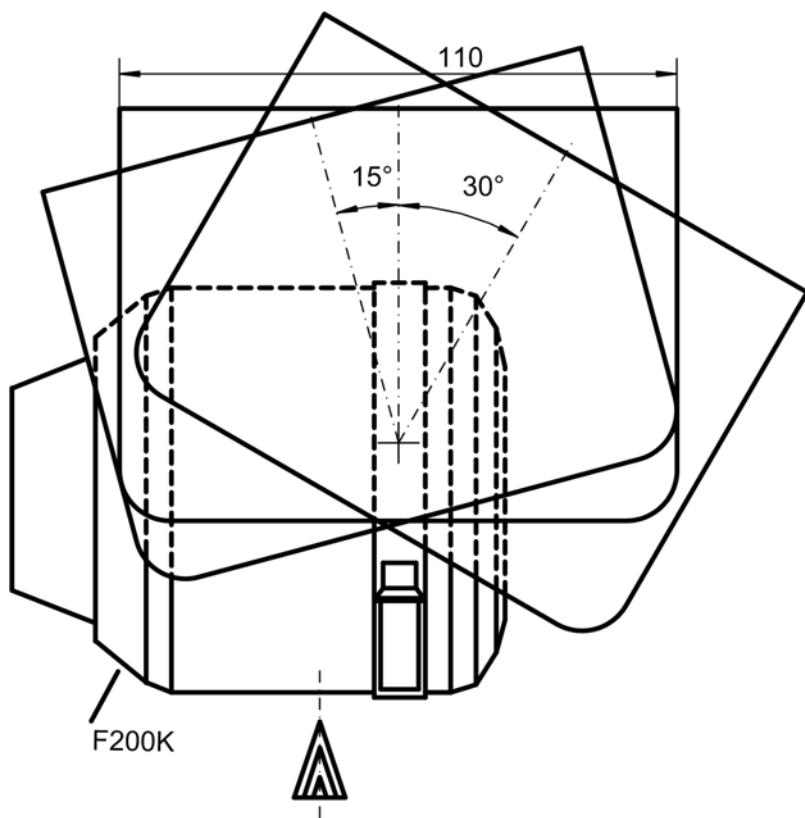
Montagevarianten des Wetterschutzes Typ 659 R 6030 (Seitenansicht)
